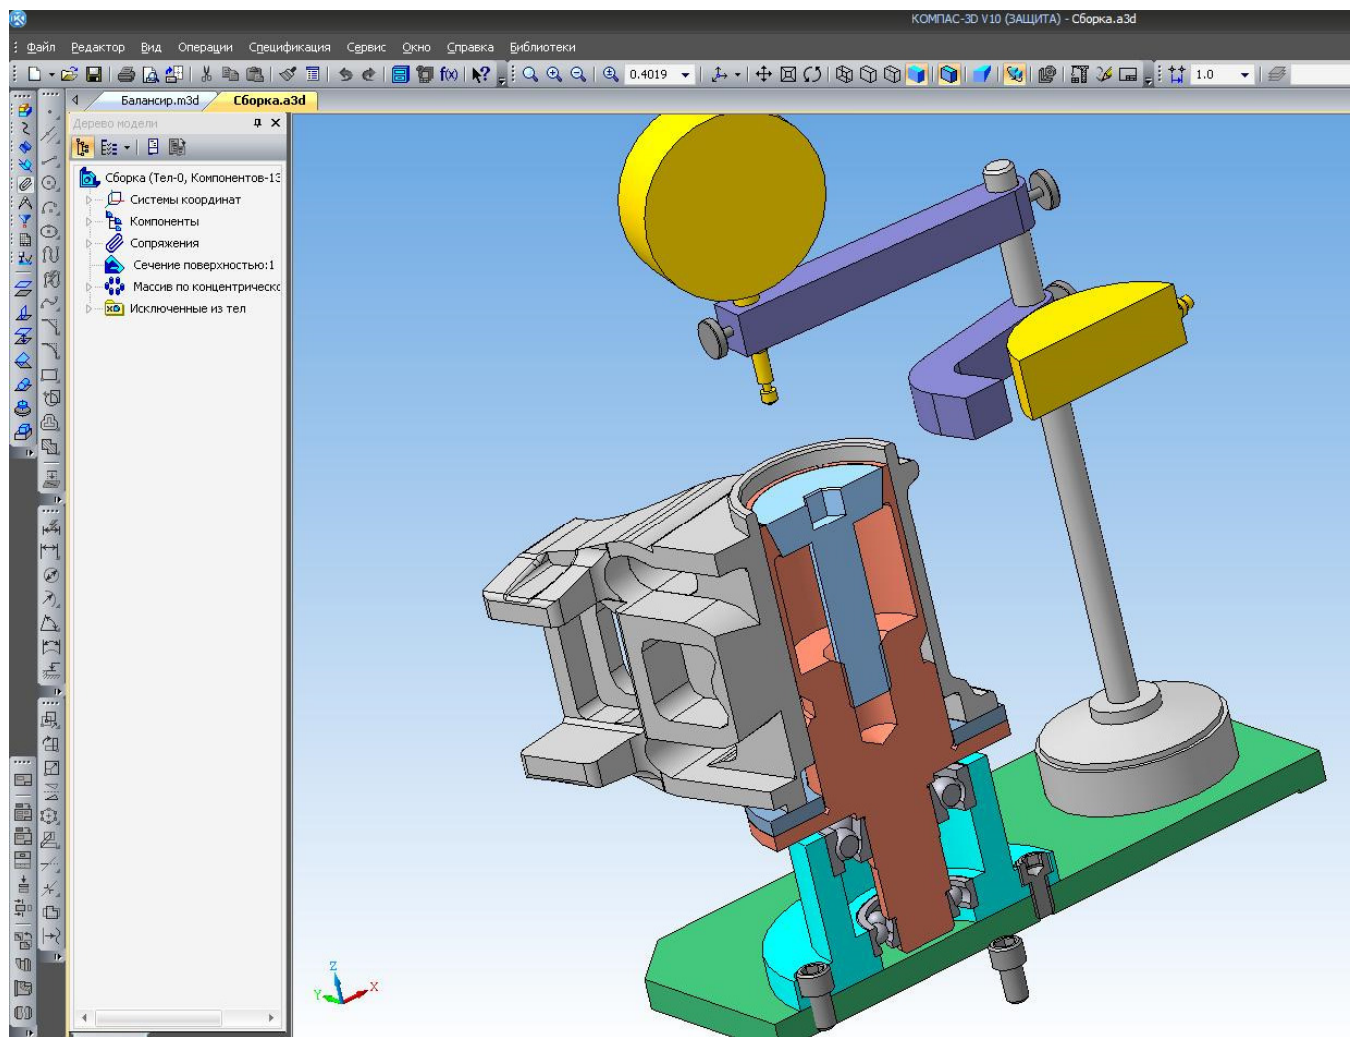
3D модель контрольного приспособления в разрезе
